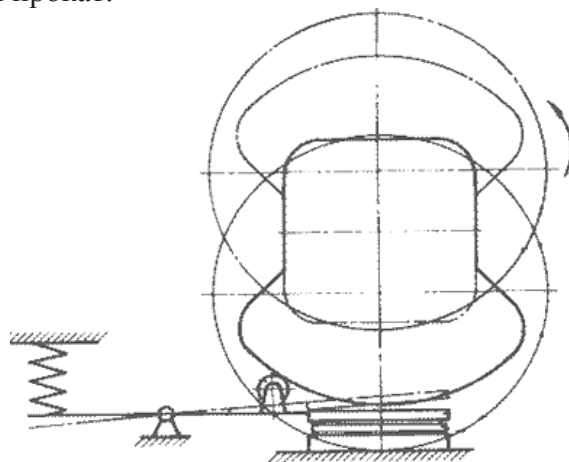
Механизм зажима профилей и кулачкообразный выступ корпуса
